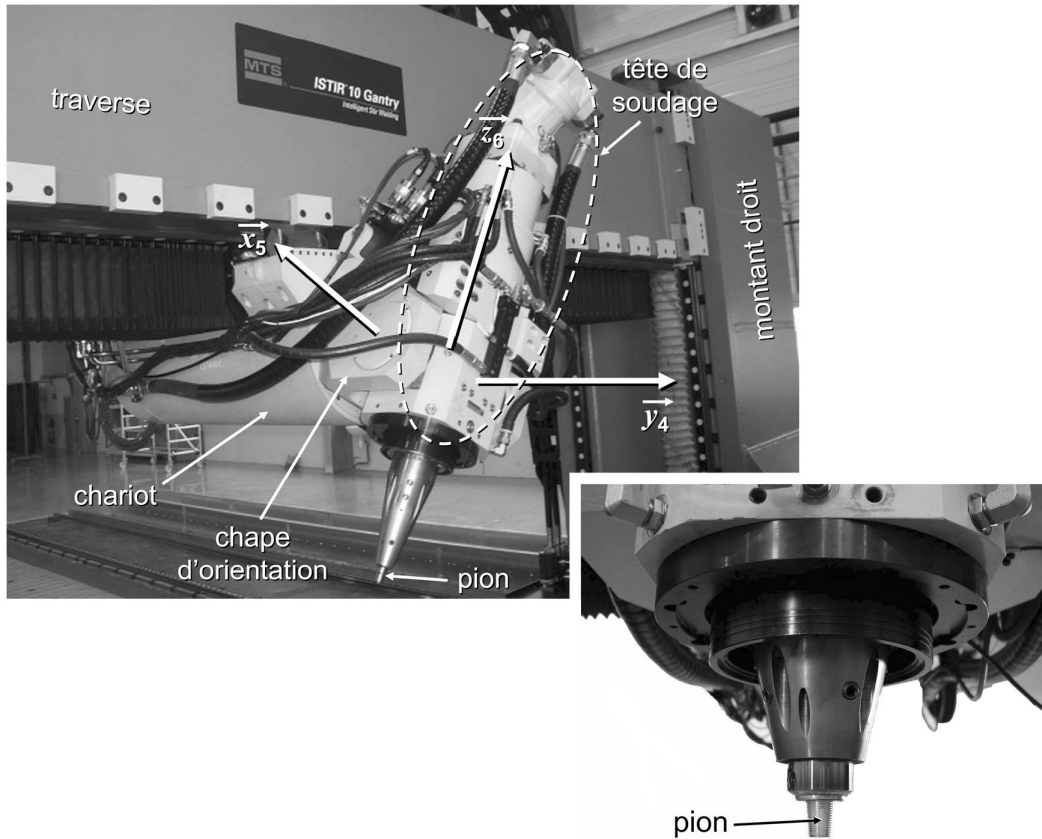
Détail de la tête de soudage de la machine "FSW".
